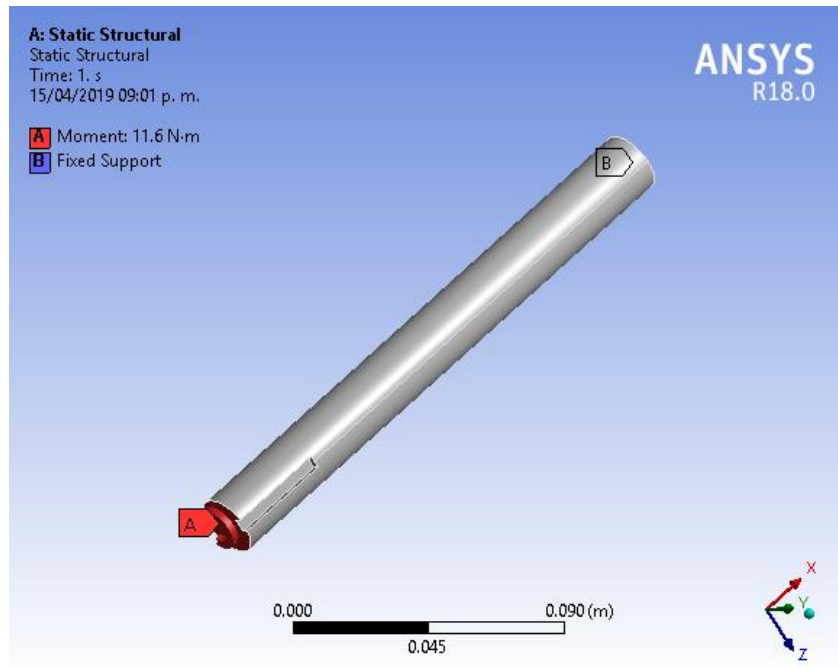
Condiciones de frontera de la flecha de motor en ANSYS WORKBENCH 18®.
